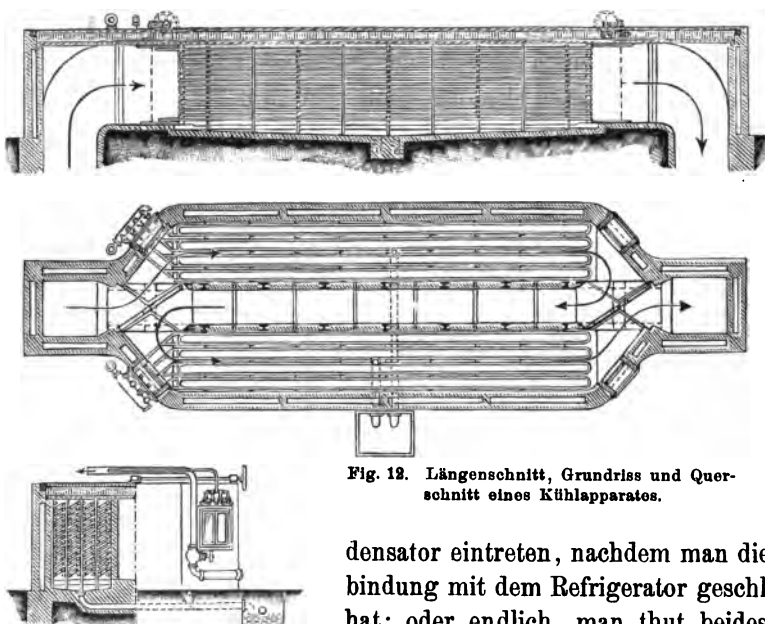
Längenschnitt, Grundriss und Querschnitt eines Kühlapparates.
